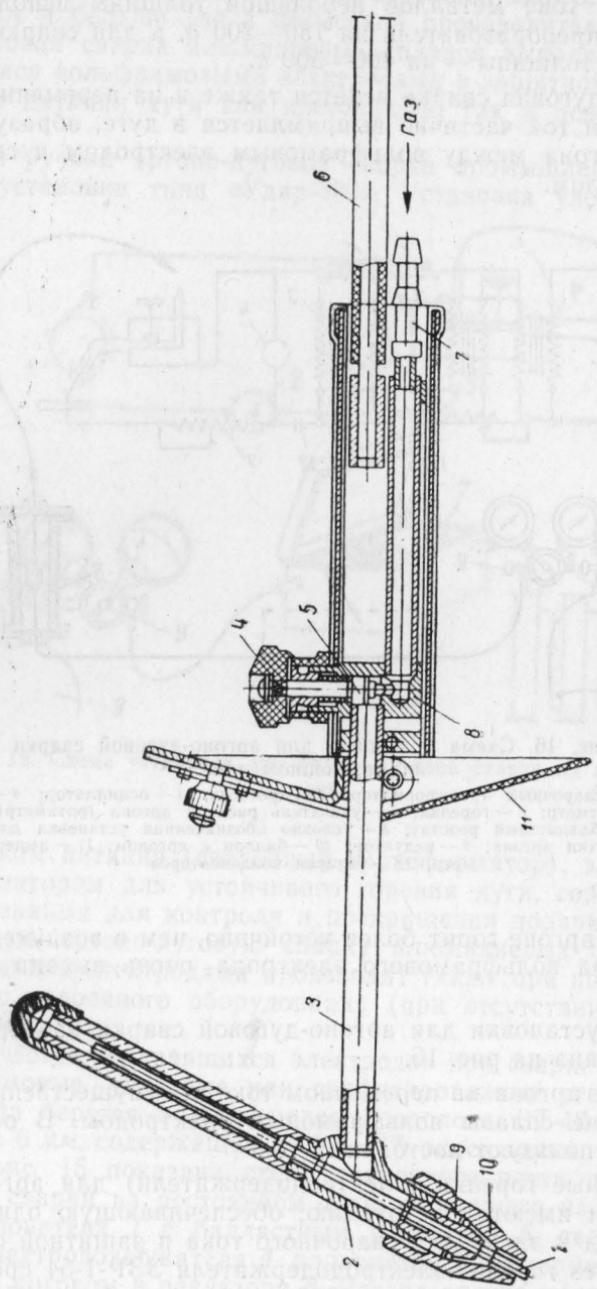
Сварочная горелка для аргоно-дуговой сварки
